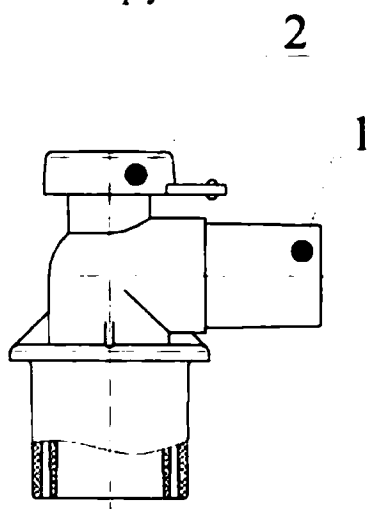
Соединитель угловой 22M/15F-15M без портов
